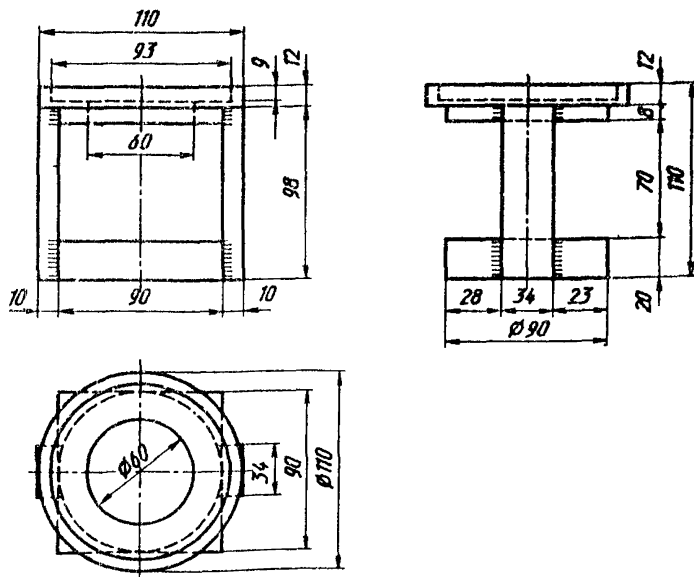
Подставка для выдавливания образцов-цилиндров (размеры даны в миллиметрах)
